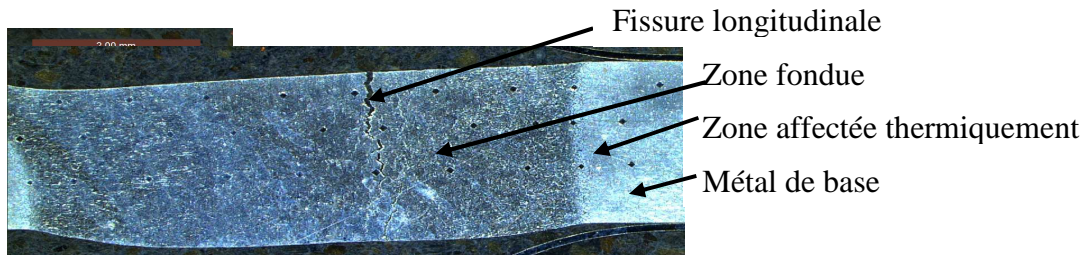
Cordon de soudure en coupe observé au microscope.
